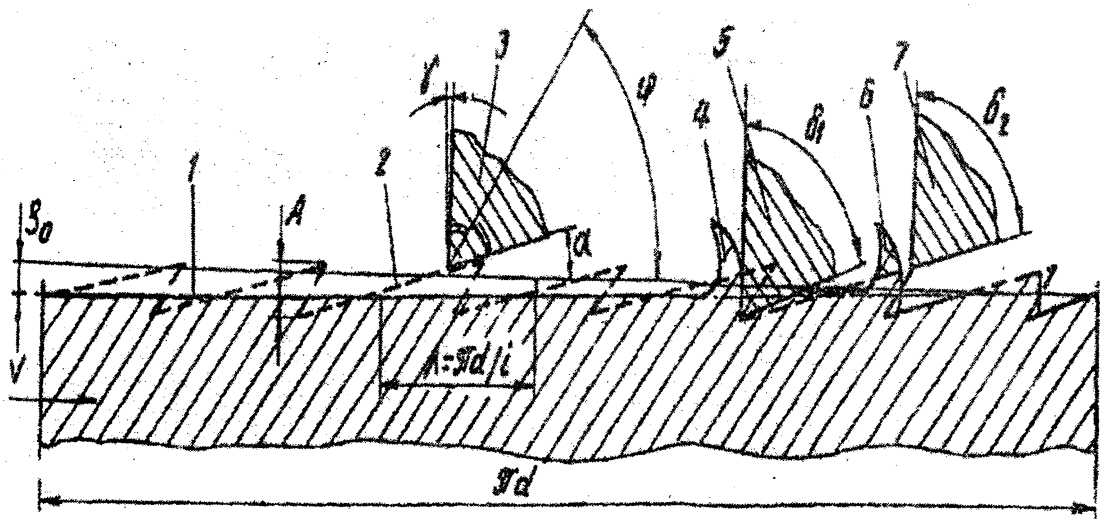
Кинематика перемещения режущих клиньев сверла при вибросверлении
